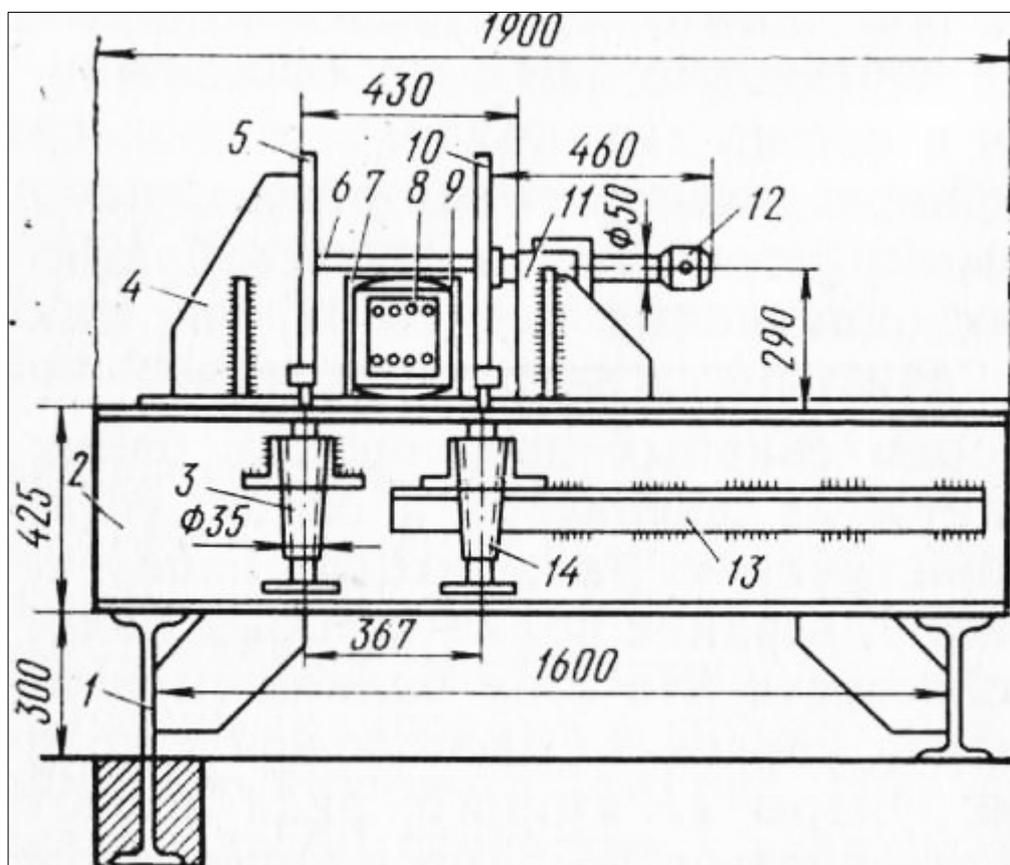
Винтовой кондуктор для сборки сварных двутавровых балок: 1 — рама, 2 — поперечная балка рамы, 3, 14 — винты, 4, 11 — неподвижный и подвижный упоры, 5, 10 — полки собираемого двутавра, 6 — стенка собираемого двутавра, 7, 8, 9 — элементы опоры под стенку собираемого двутавра, 12 — винт подвижного упора, 13 — направляющий уголок подвижного упора.
